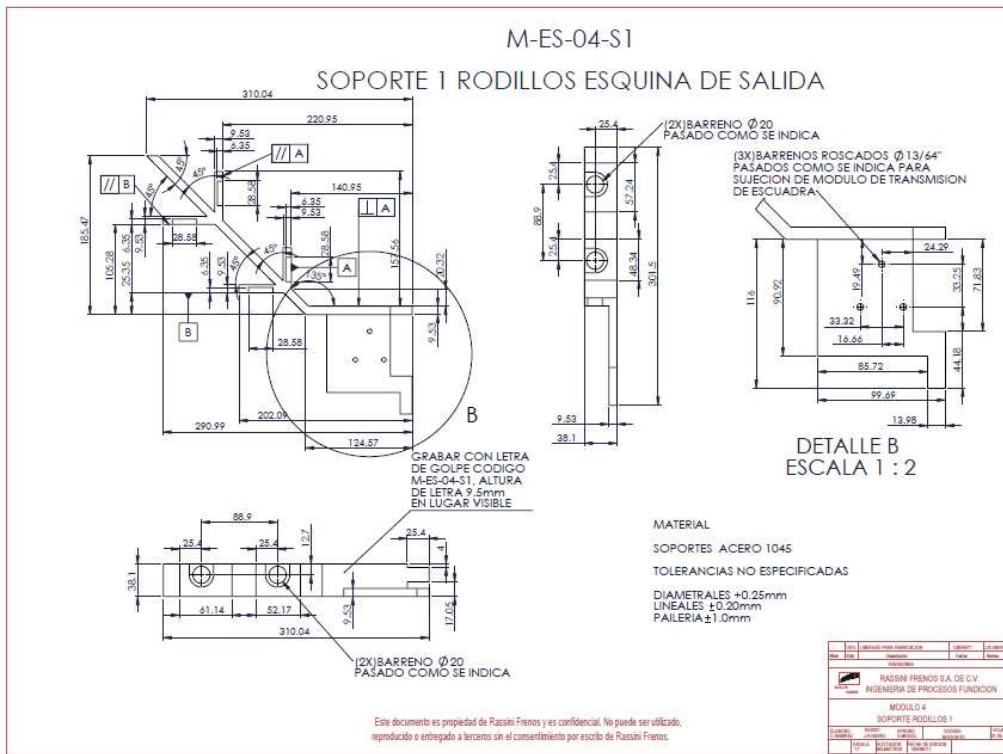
Plano de fabricación soporte 1 para rodillos
